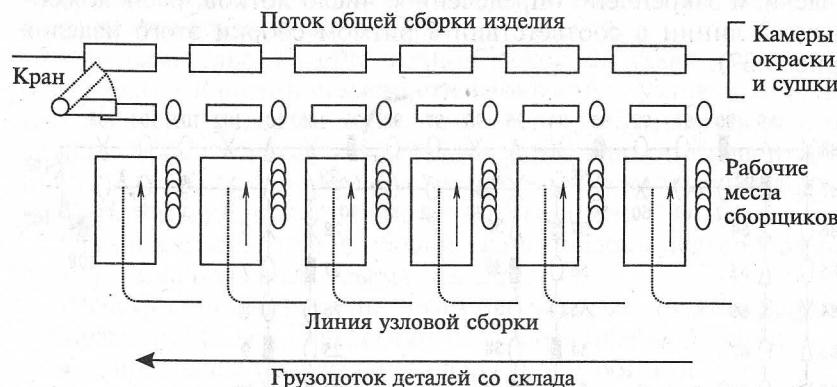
План-схема потоков узловой и общей сборки изделия
